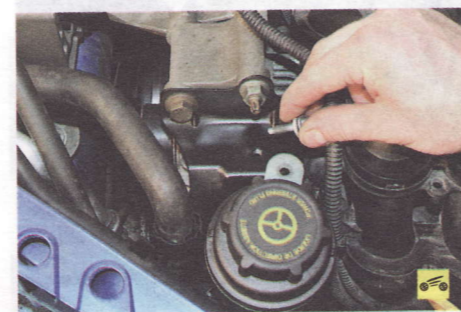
Крепление генератора: 1 – верхний болт крепления генератора; 2 – шпилька крепления генератора; 3 – гайка; 4 – защитный щиток; 5 – нижний болт крепления генератора
